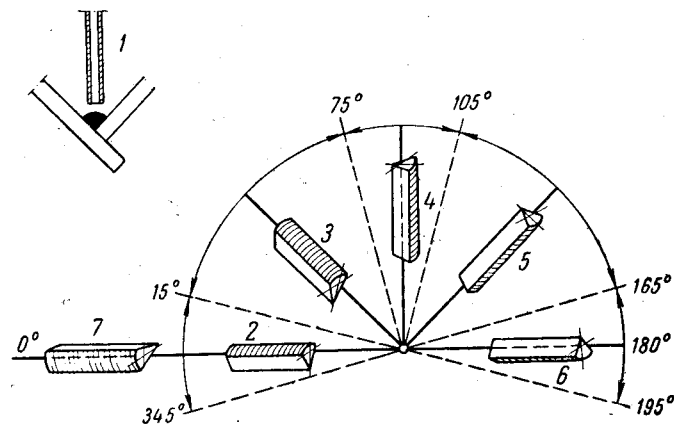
Классификация сварных швов по пространственному расположению при выполнении сварки.
